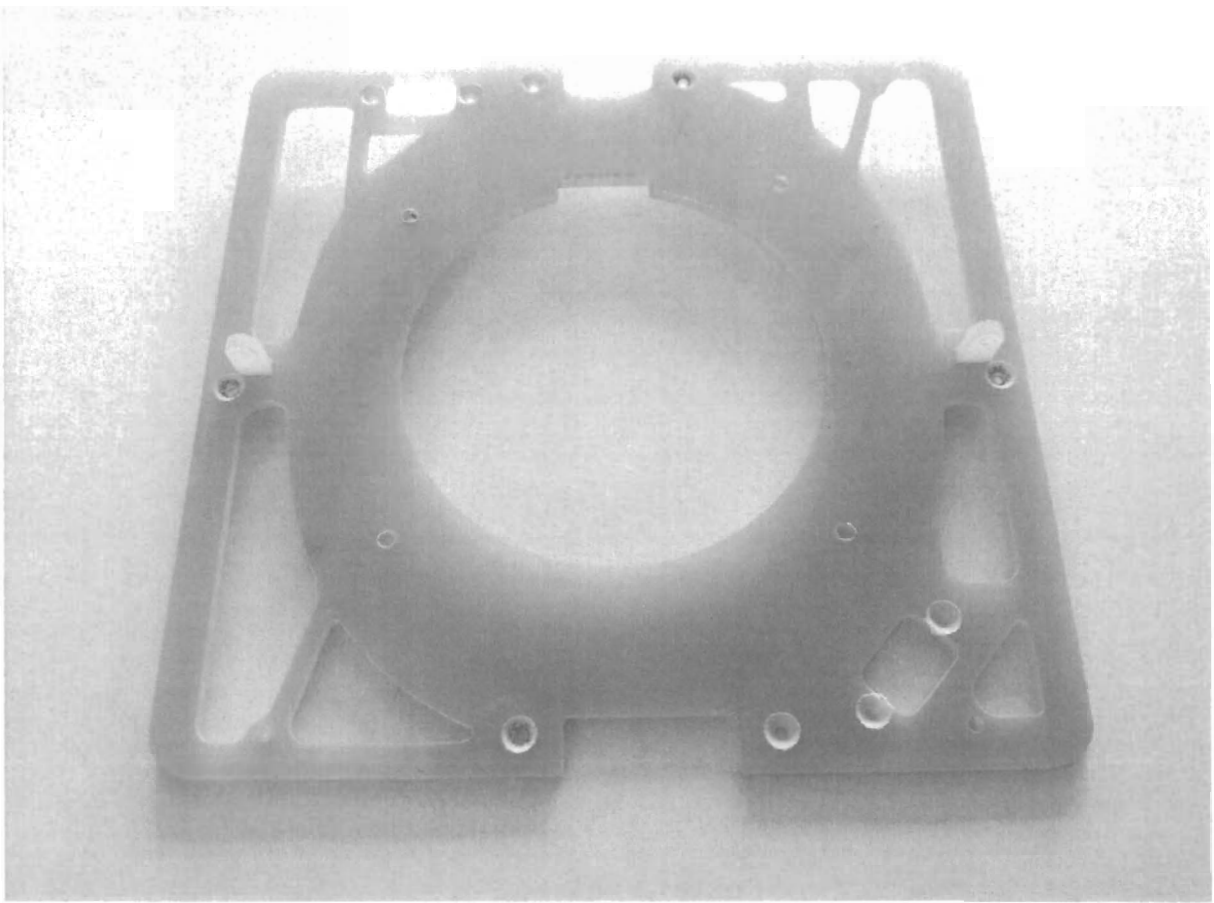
Cadru rigidizat – zona de prindere a PCB-ului
